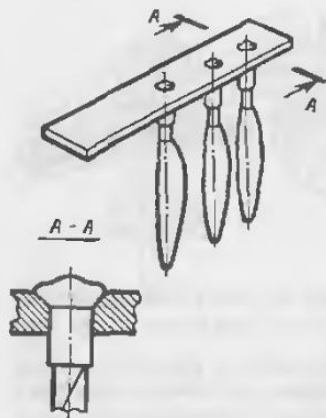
Приспособление для цветного анодирования готовых лопастей из алюминиевого сплава
